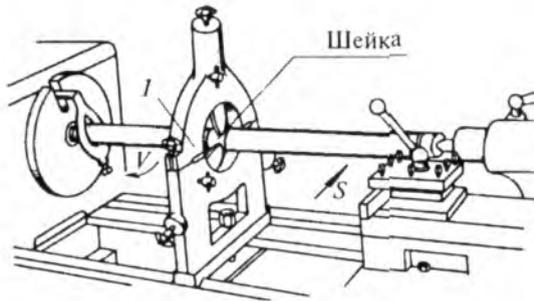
Обработка длиномерных заготовок с использованием неподвижного люнета:
